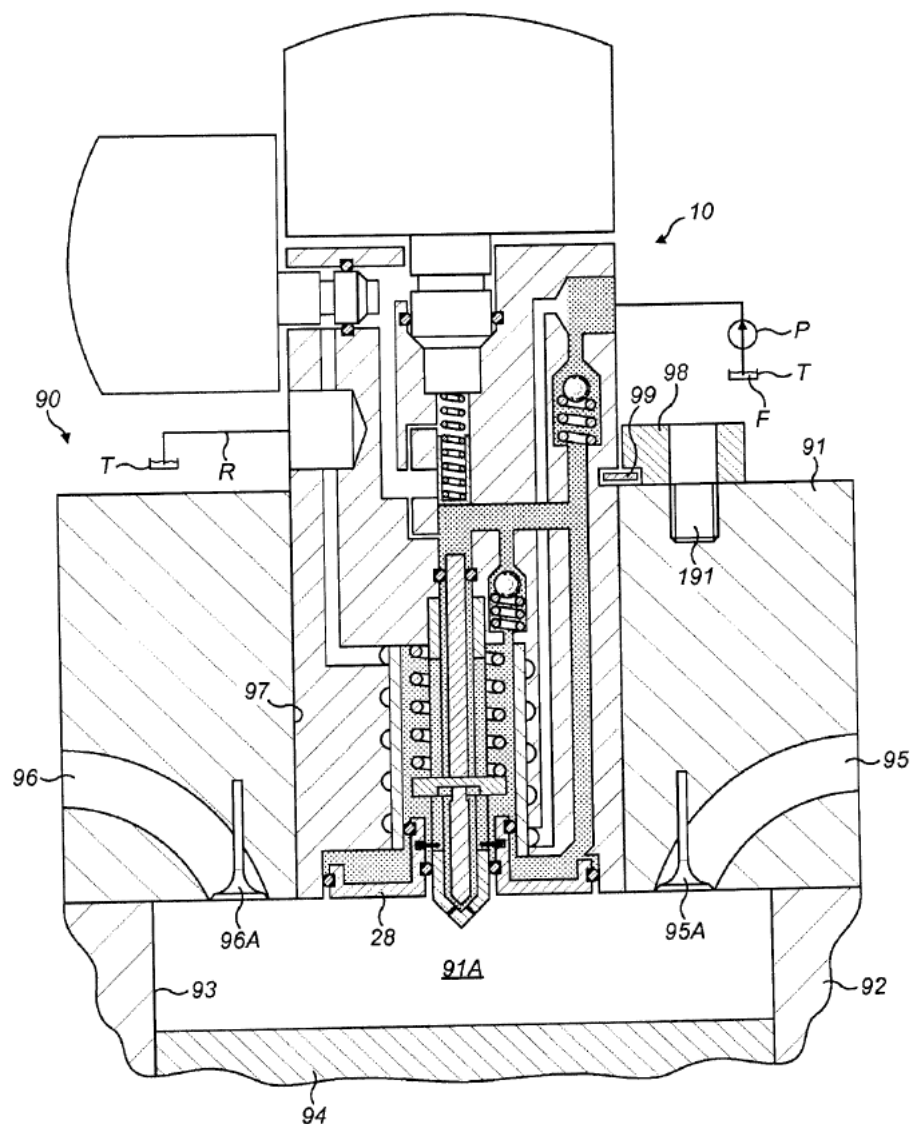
Принципова схема розташування форсунки у циліндрі
